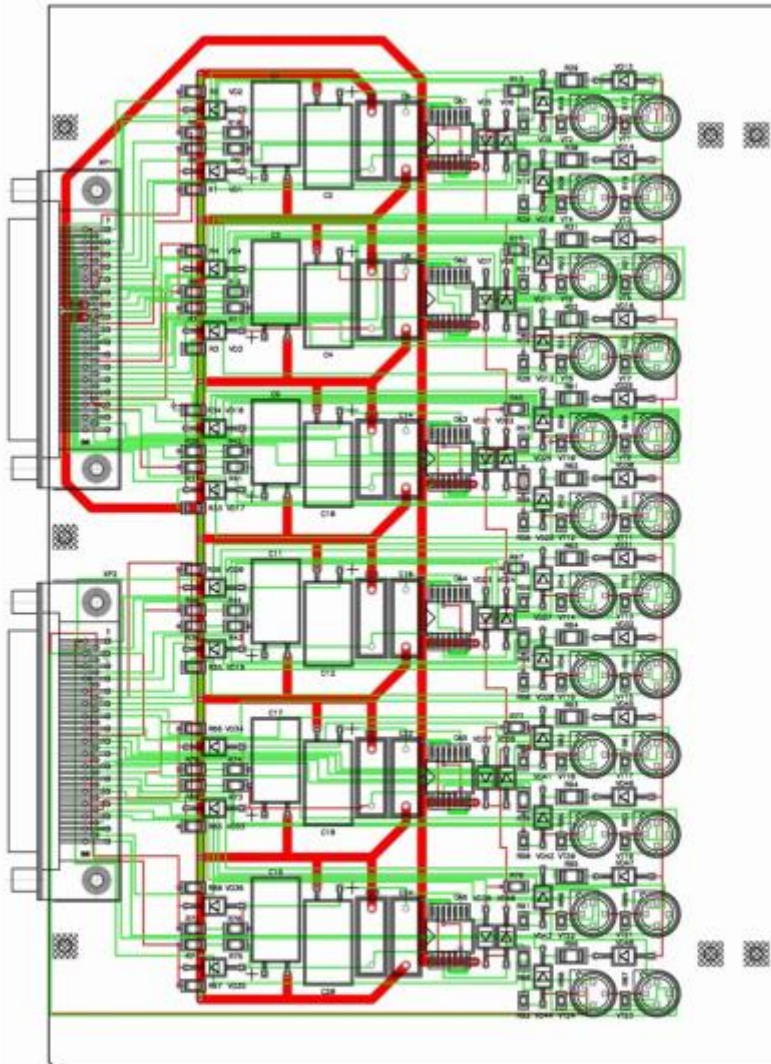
Автотрассировка, Allegro PCB Router
